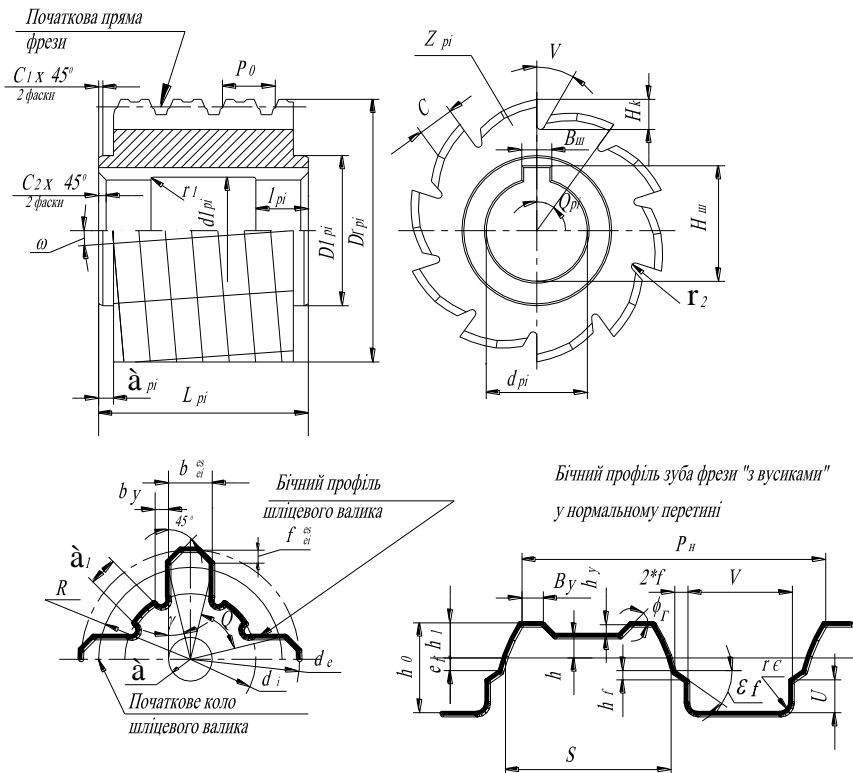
Черв'ячно-шліцева фреза "з вусиками", профіль шліцевого валика виконання А і бічний профіль зуба фрези у нормальному перетині.
